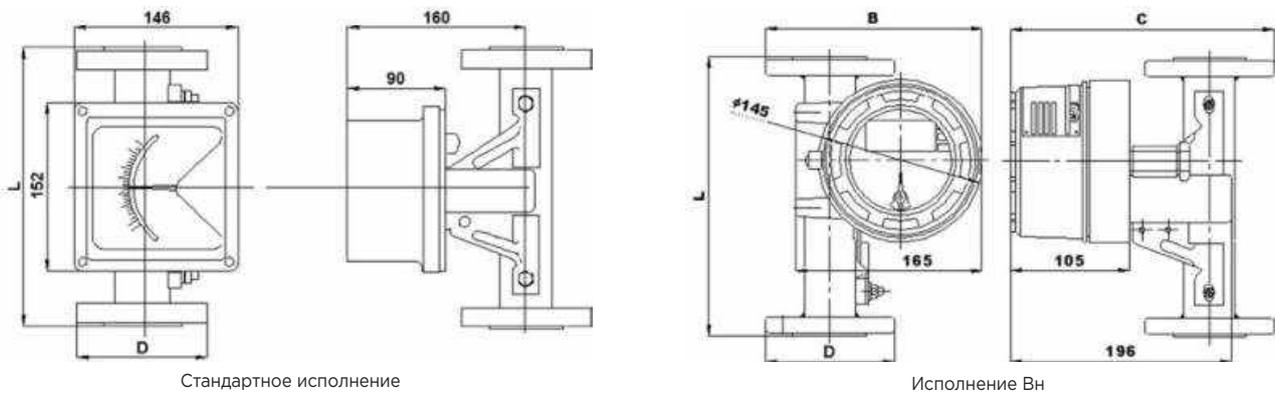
Габаритные и присоединительные размеры ротаметров с фланцевым соединением
